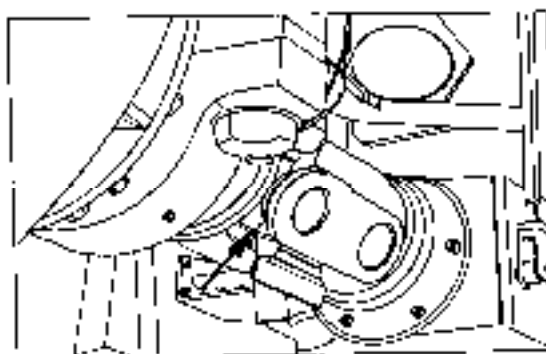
Масленка вала «коробка передач – задний мост»
